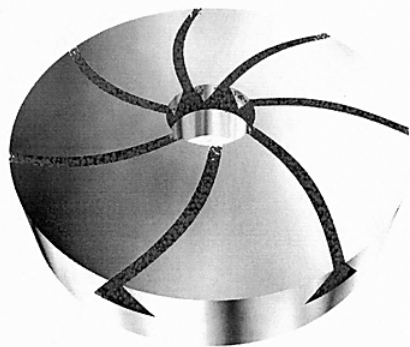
Чашечный цилиндрический композиционный шлифовальный круг
